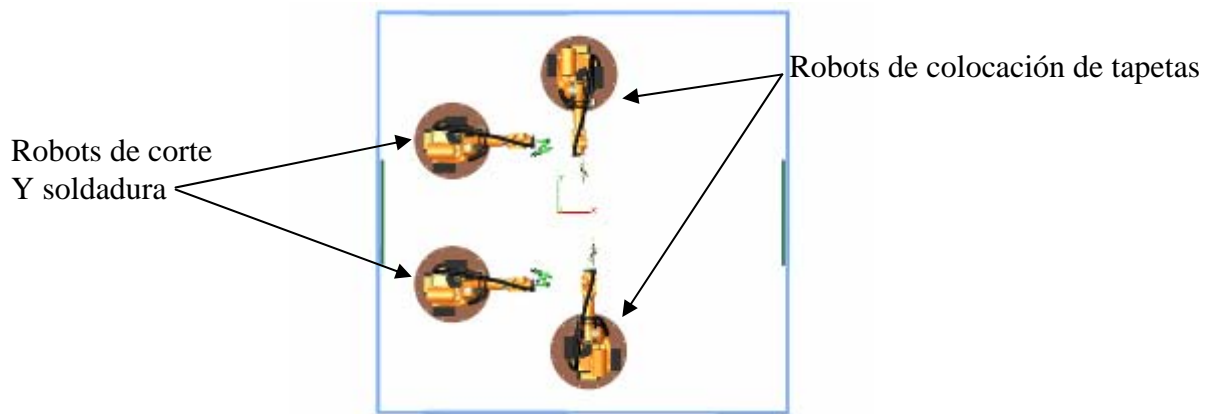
Situación de los robots dentro de la cabina de soldadura
